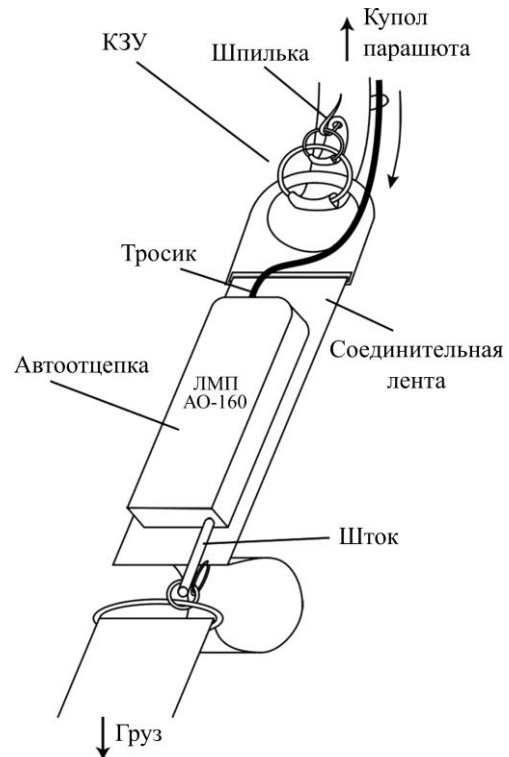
Эскиз разработанной конструкции устройства автоотцепки
